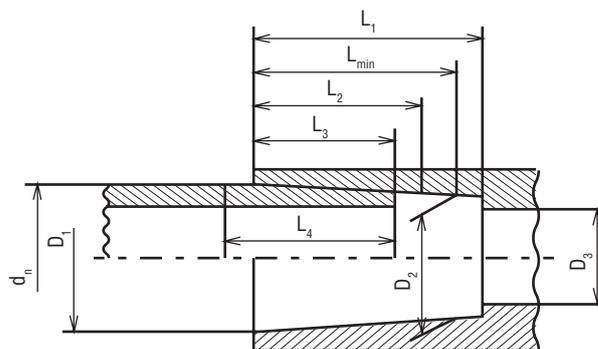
Габаритные размеры раструба сварных фитингов.
